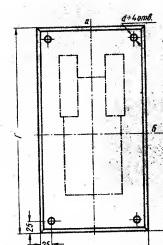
Габаритные размеры изоляционных плит для контакторов серии КТП-500
